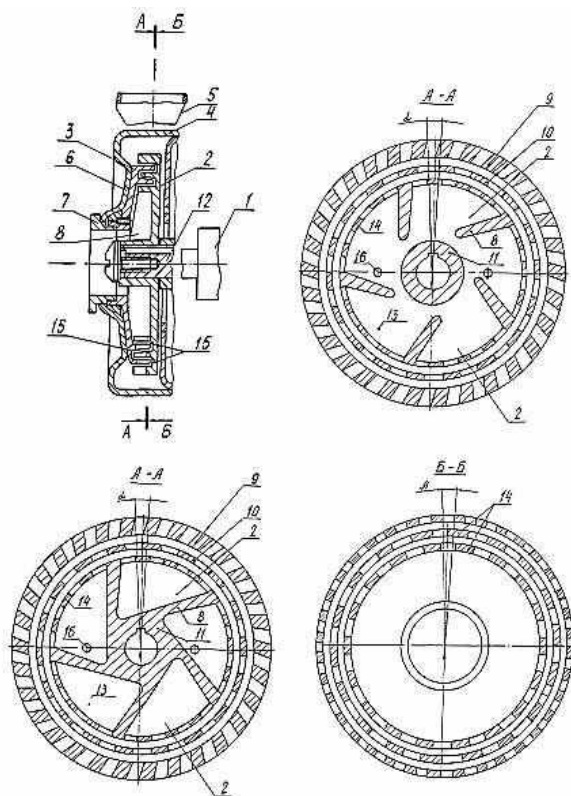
Загальний вигляд і в розрізі по перерізах РПА: 1 – привід; 2 – ротор; 3 – статор; 4 – корпус; 5 – випускний патрубок; 6 – кришка; 7 – впускний патрубок; 8 – вхідні лопатки насоса; 9 – вихідні лопатки насоса; 10, 14 – зубчастий елемент; 11 – маточина; 12 – вал; 13 – камера; 15 – кільцеві канавки; 16 – розвантажувальні отвори
